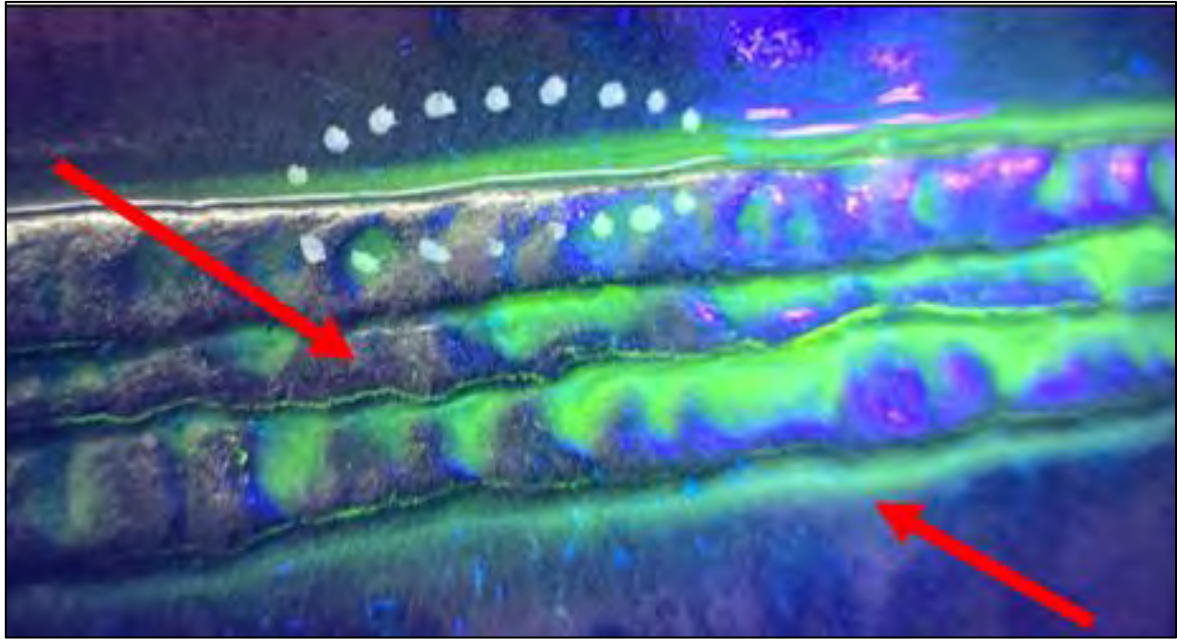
Indicaciones lineales en el cordón de soldadura
